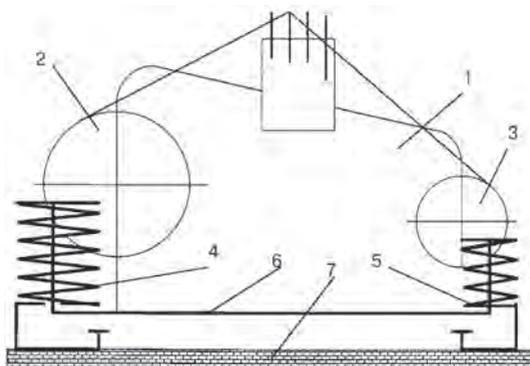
Расчетная схема системы виброизоляции для пневматических ткацких станков типа PN 130: 1–станок; 2–навоя; 3–товарный валик; 4,5–резиновые виброизоляторы со стороны навоя станка и со стороны грудницы; 6–опорная поверхность станка; 7–межэтажное перекрытие.
